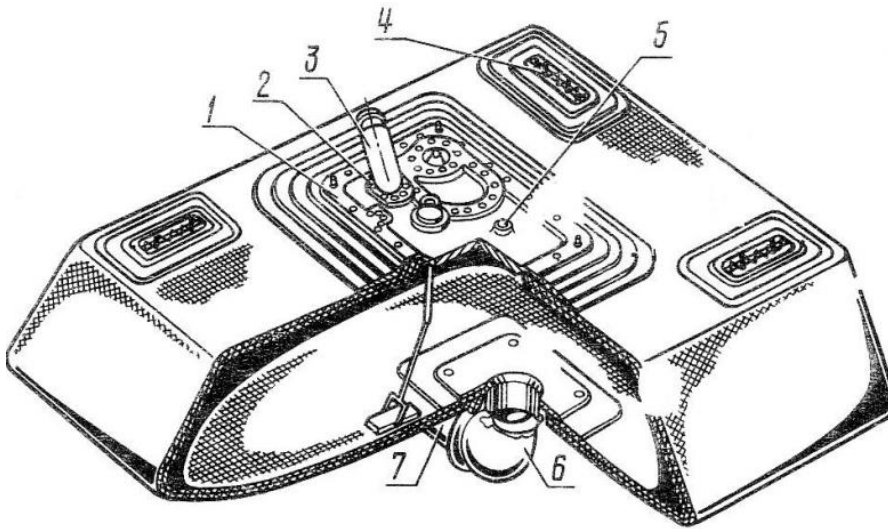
Расходный топливный бак вертолета Ми-8: 1 – плита; 2 – датчик топливомера; 3 – патрубок заливной горловины; 4 – шпилька крепления к контейнеру; 5 – дренажный штуцер; 6 – переходник; 7 – насос 463Б
